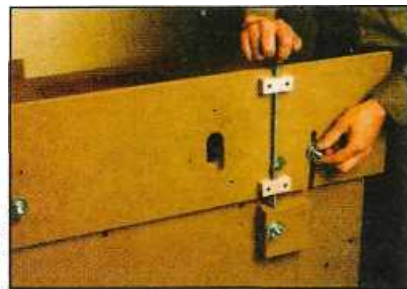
Конструкция опоры для горизонтального положения фрезера.
